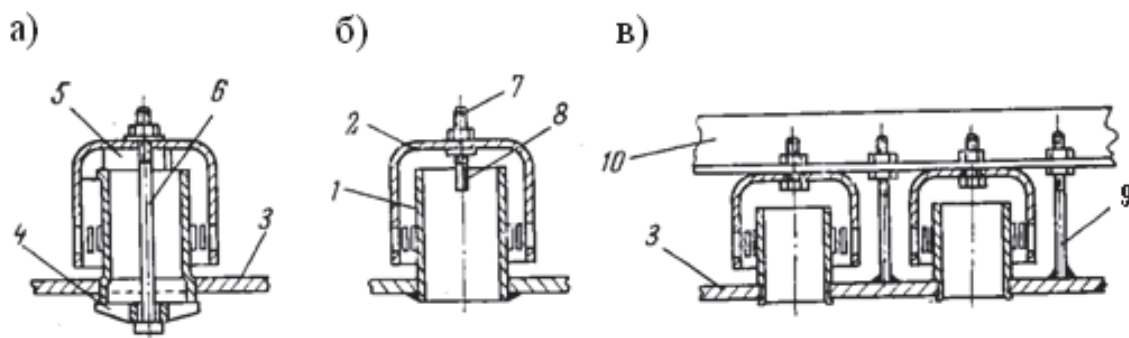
Типы крепления колпачков: а, б – индивидуальные крепления; в – крепление групповое (гирляндой); 1 – стакан; 2 – колпачок; 3 – диск тарелки; 4 – трубка; 5, 8 – планки; 6 – болт; 7 – шпилька; 9 – штырь; 10 – несущий уголок
